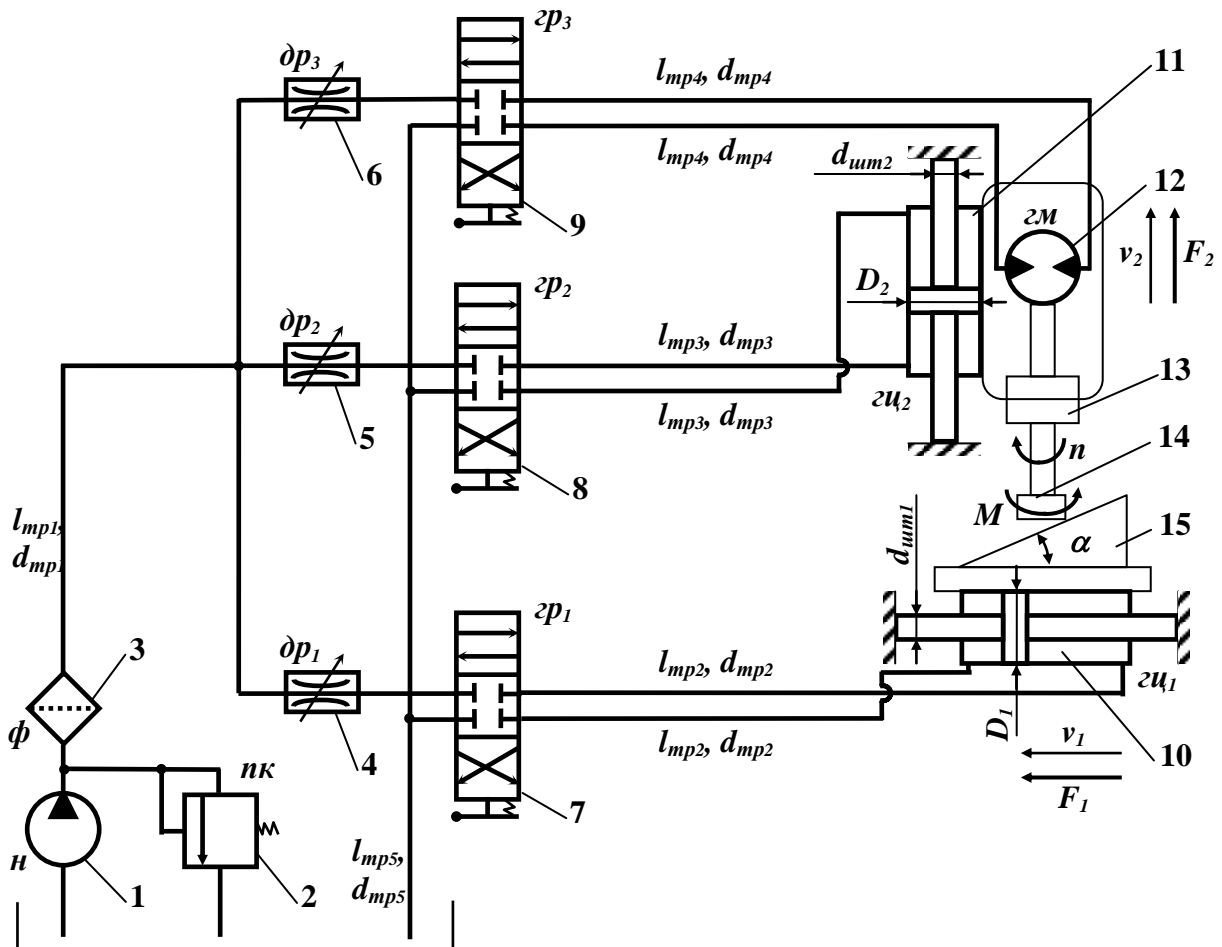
Принципиальная схема гидропривода фрезерного станка
